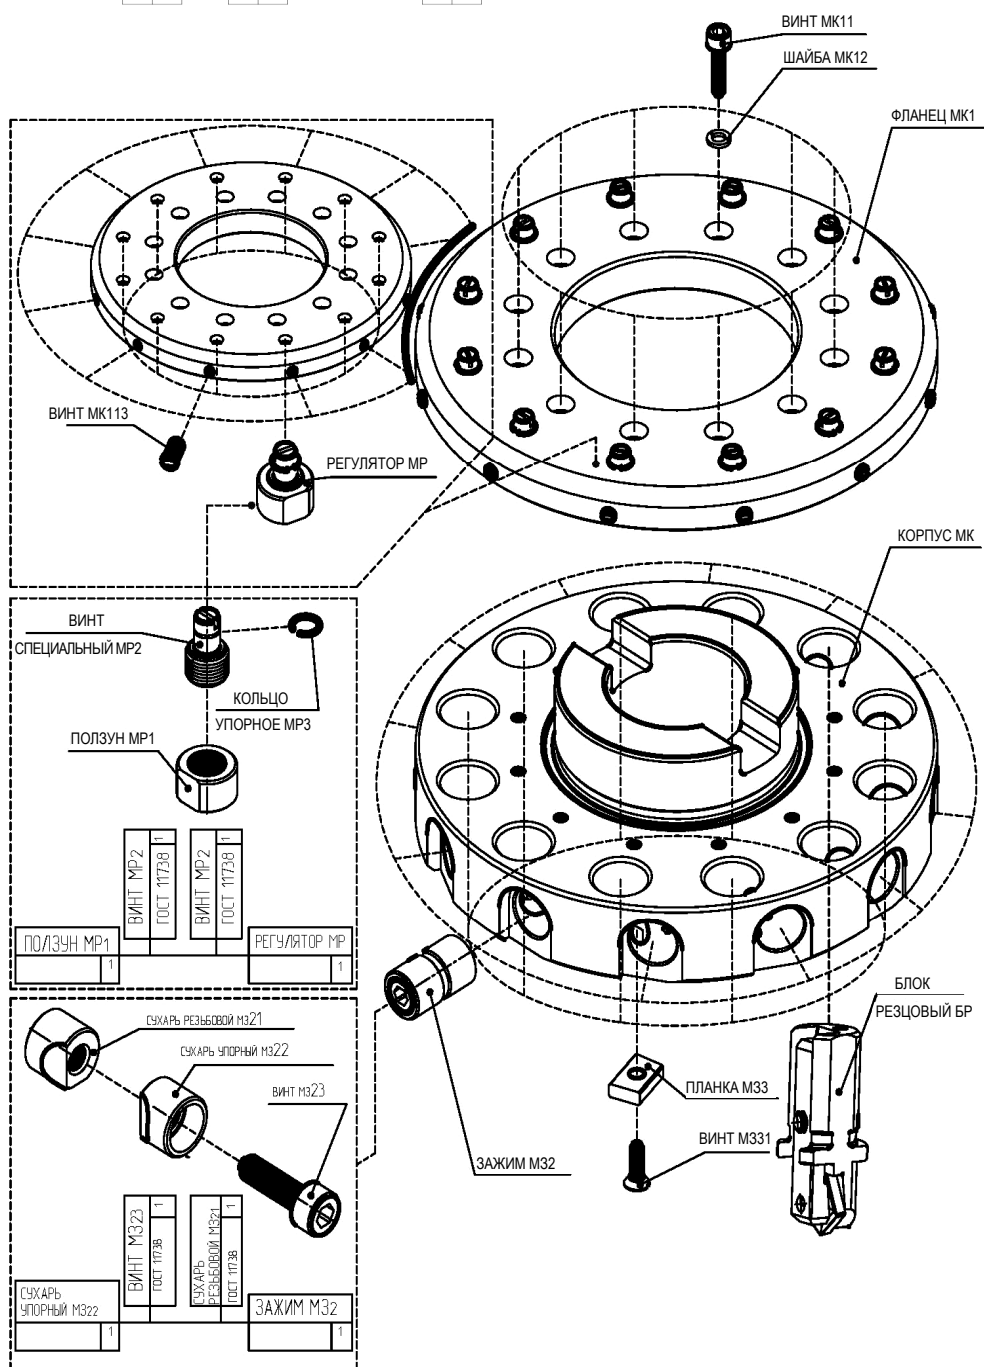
Технологическая схема сборки фрезы торцовой
